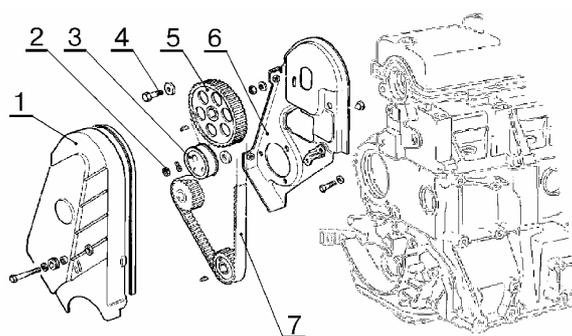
Механизм привода ГРМ двигателя ВАЗ-21114:
